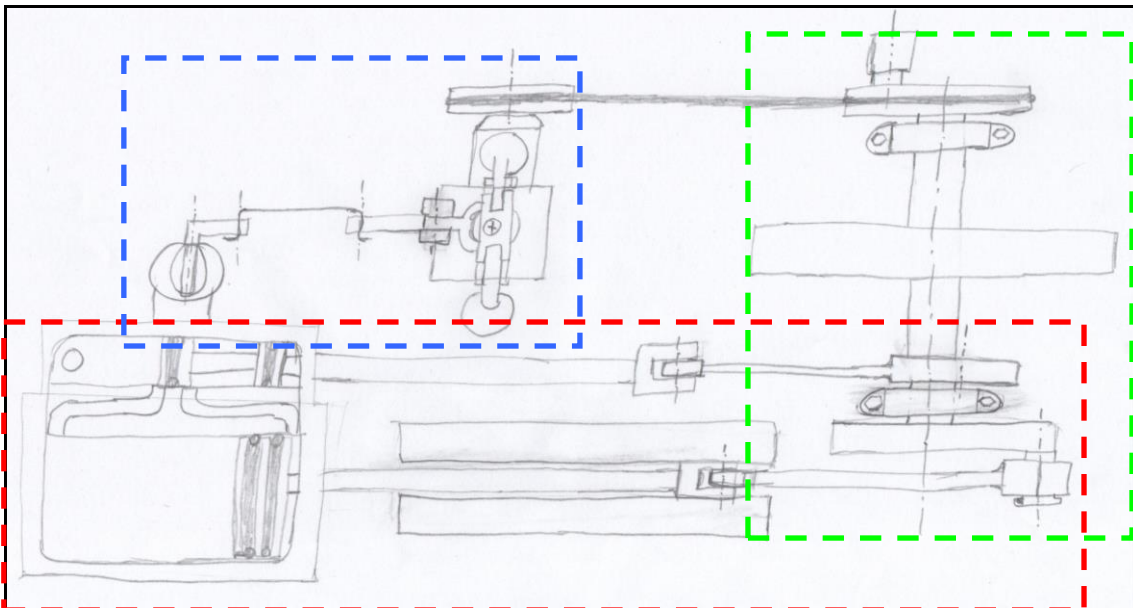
Croquis con los diferentes subensamblajes: motor (rojo), eje máquina (verde) y regulador (azul).
